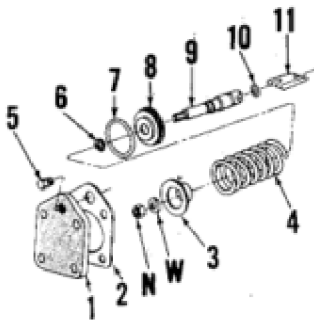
Geëxplodeerde mening van Servo 1 assemblage.
